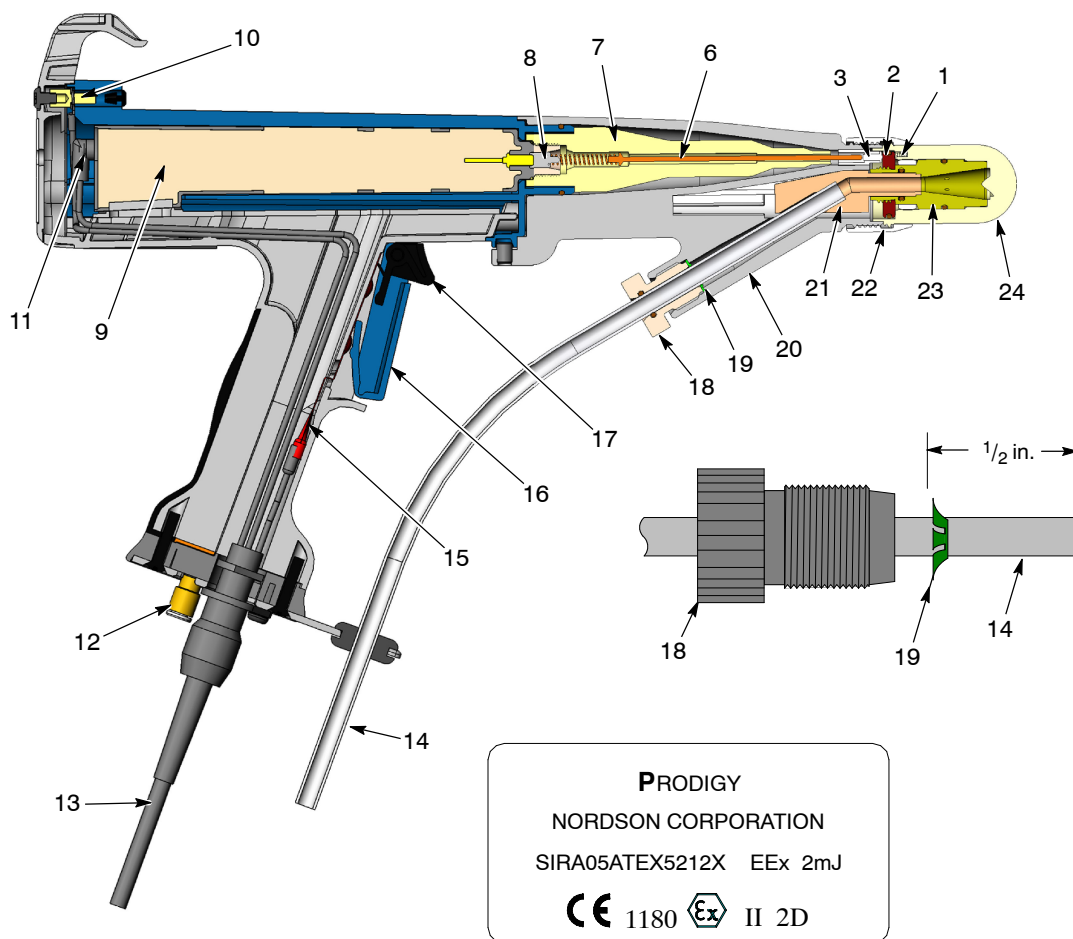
Przekrój pistoletu proszkowego o standardowej długości.
